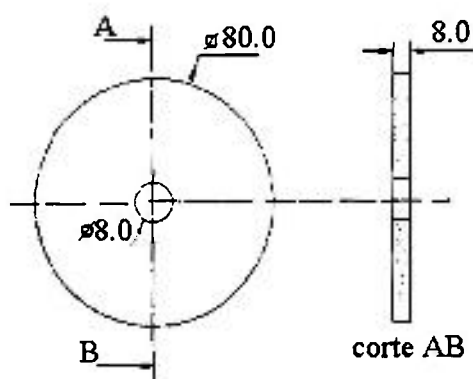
Geometria e dimensões do disco de ferro fundido.
